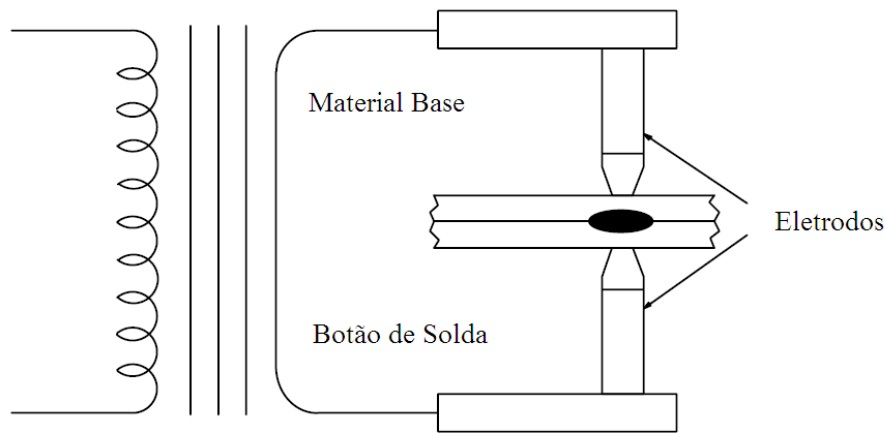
desenho esquemático de uma máquina de solda ponto.
